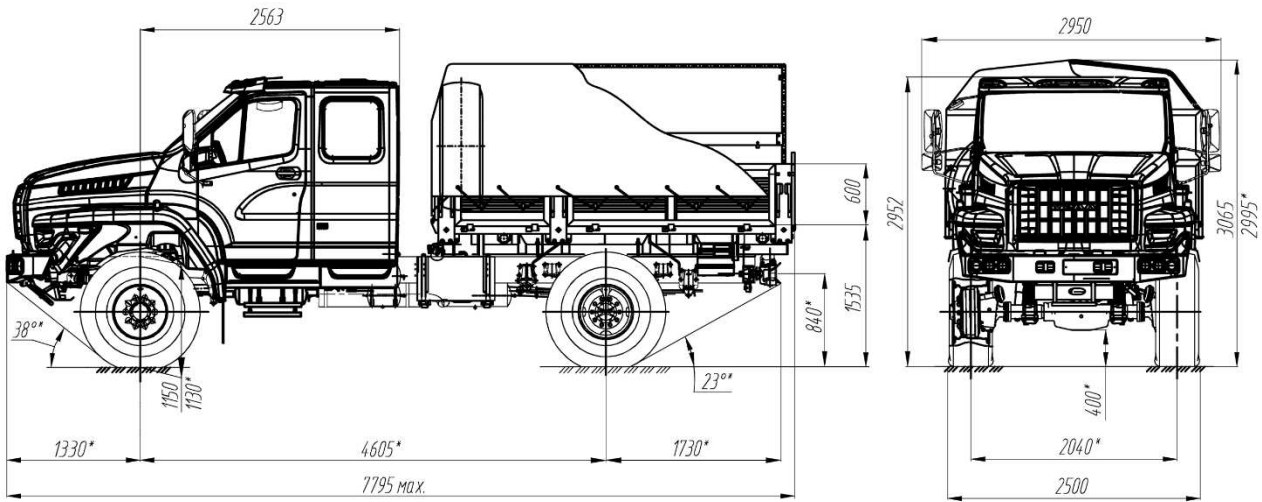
Габаритные размеры автомобиля Урал-43206-5551-71/73
